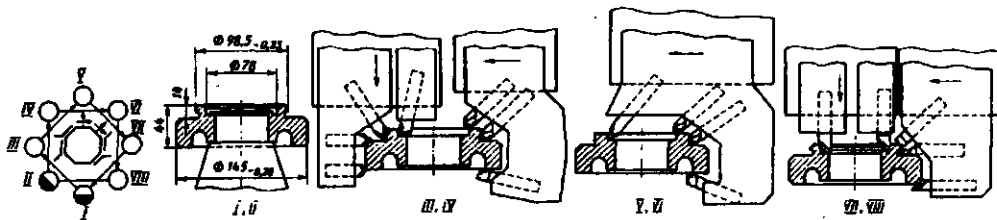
Наладка восьмишпиндельного полуавтомата для двухцикловой обработки заготовок зубчатых колес
